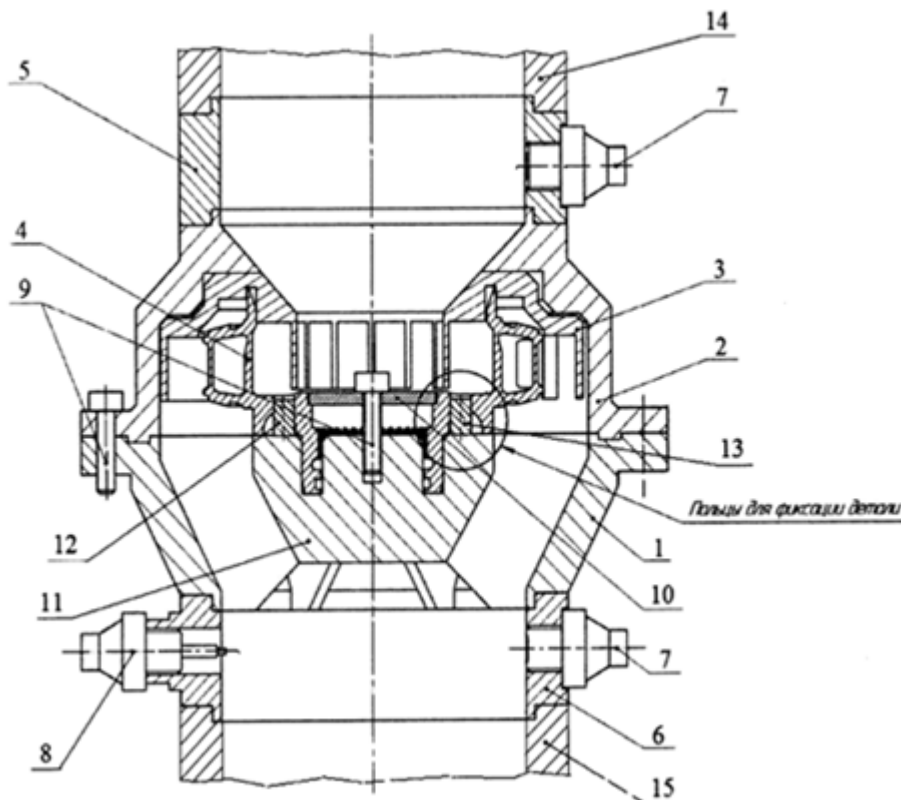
Способ обработки абразивным потоком межлопаточных каналов крыльчаток: 1 - нижняя часть приспособления; 2 - верхняя часть приспособления; 3 - направляющий аппарат; 4 - обрабатываемая заготовка; 5 - верхний переходник; 6 - нижний переходник; 7 - датчики давления; 8 - температурный датчик; 9 - болты; 10 - стопорное кольцо; 11 - основание; 12 - цилиндрический палец; 13 - призматический палец; 14 - верхний рабочий цилиндр; 15 - нижний рабочий цилиндр
